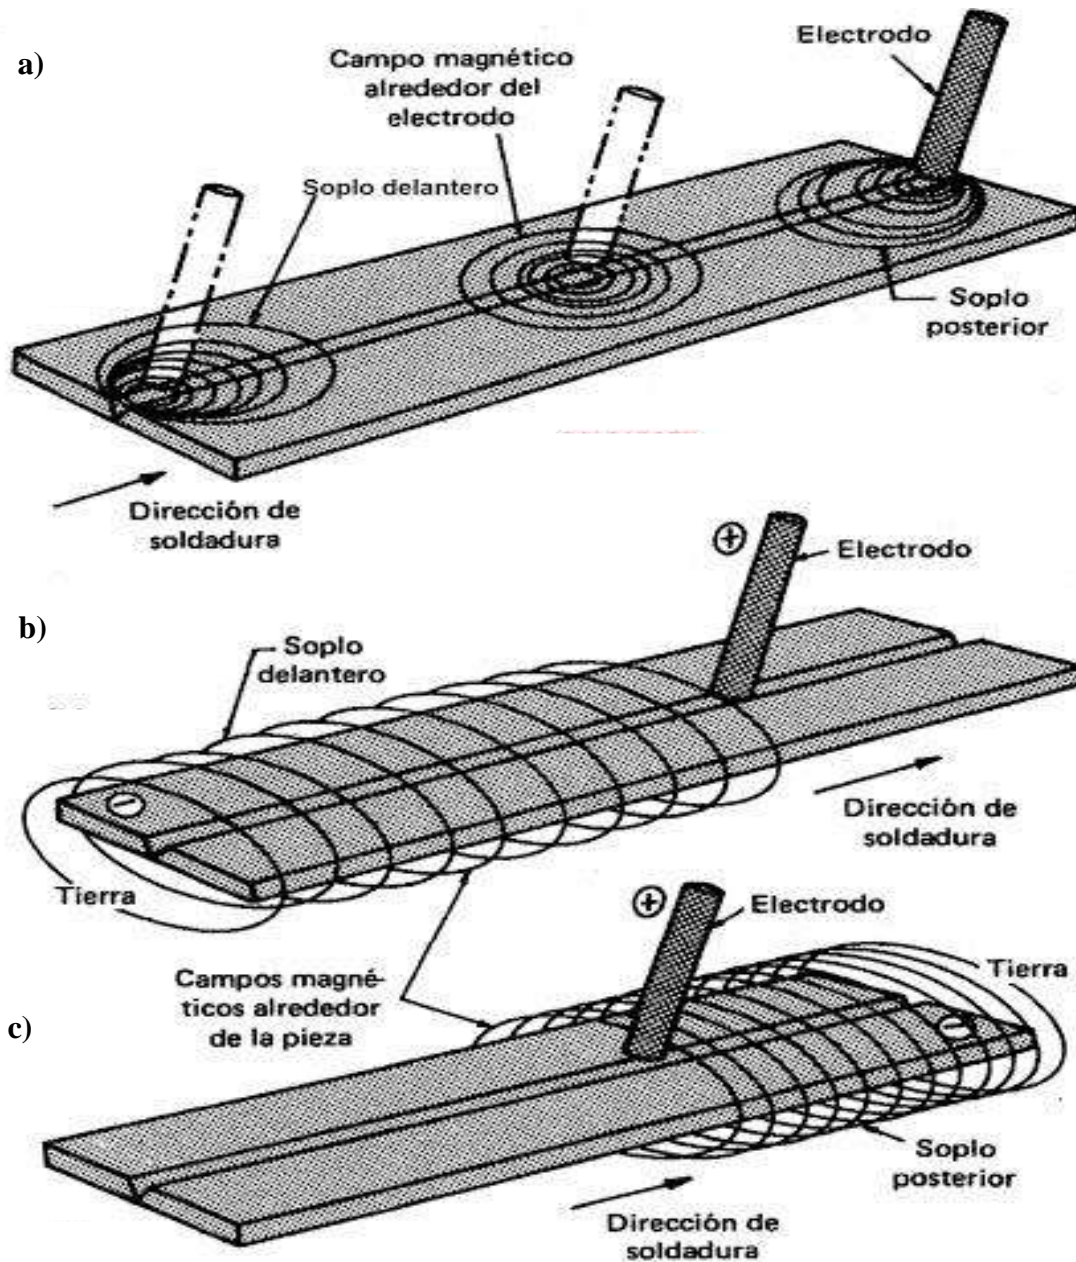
Campos magnéticos actuando en placas soldadas: a) alrededor del electrodo, b) y c) alrededor de la pieza [11]
